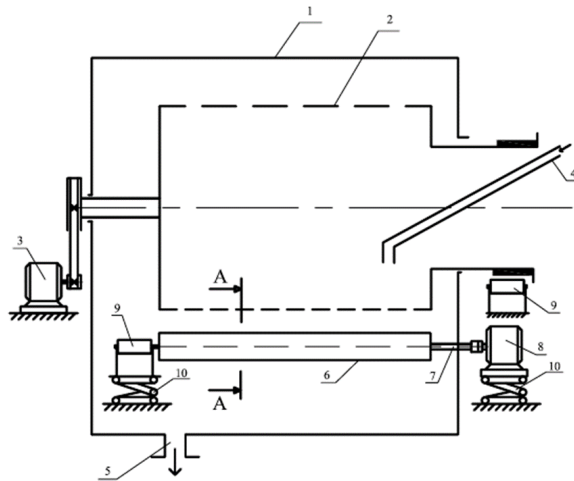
Схема общего вида предлагаемой конструкции фильтрующей центрифуги
